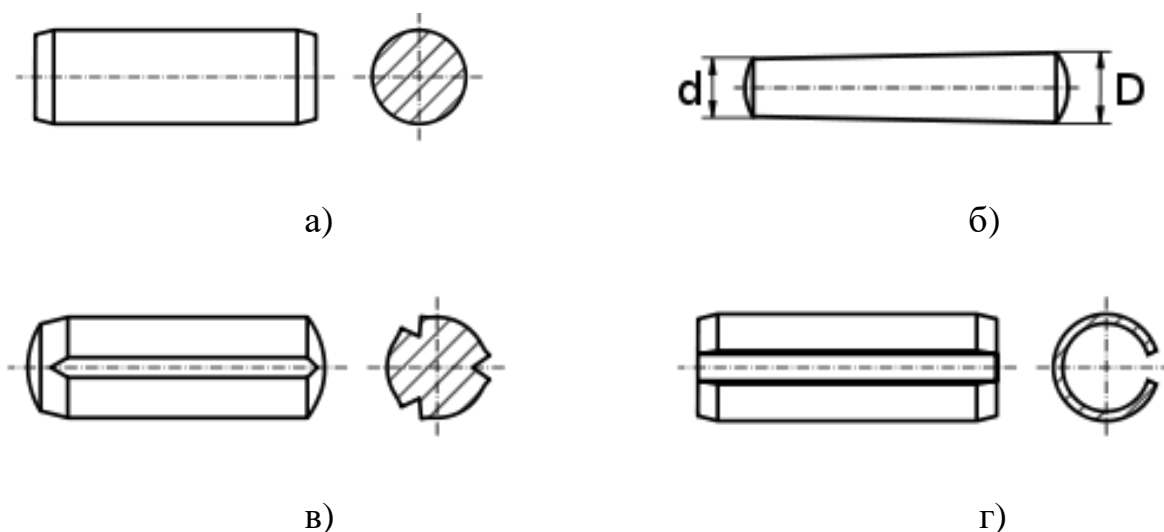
Штифти: а – циліндричний гладкий; б – конічний гладкий;
